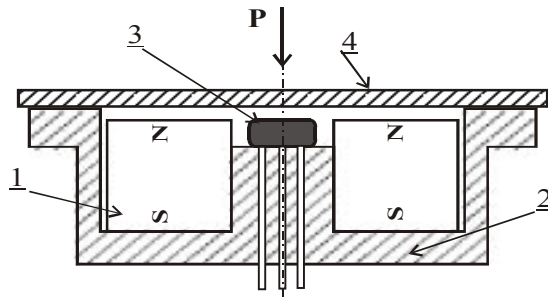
Вариант конструкции миниатюрного датчика давления: 1 – кольцевой постоянный магнит; 2 – корпус-магнитопровод; 3 – преобразователь магнитного поля; 4 – стальная мембрана
